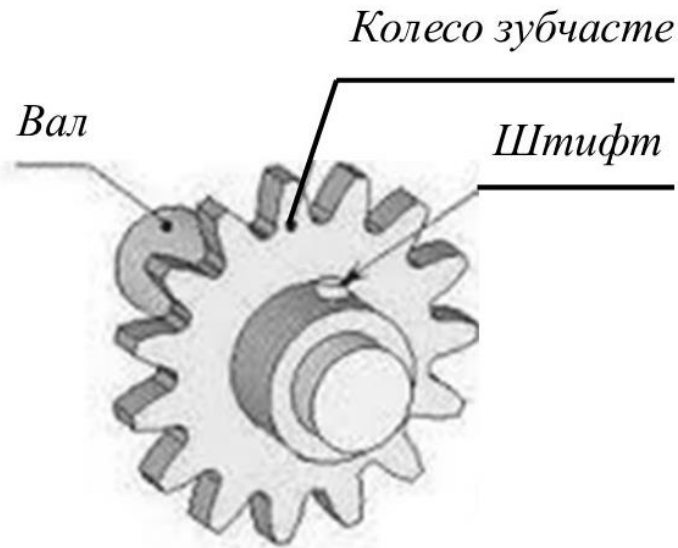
Штифтове з'єднання зубчастого колеса з валом
